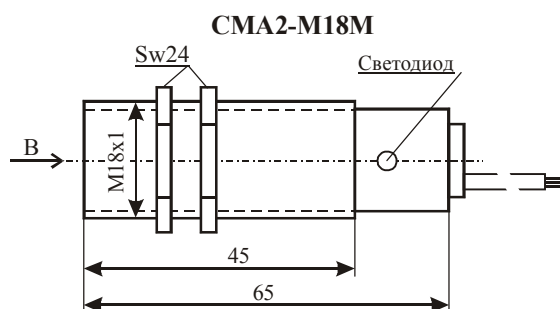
Внешний вид и габаритные размеры датчиков типа СМА2-М18М
